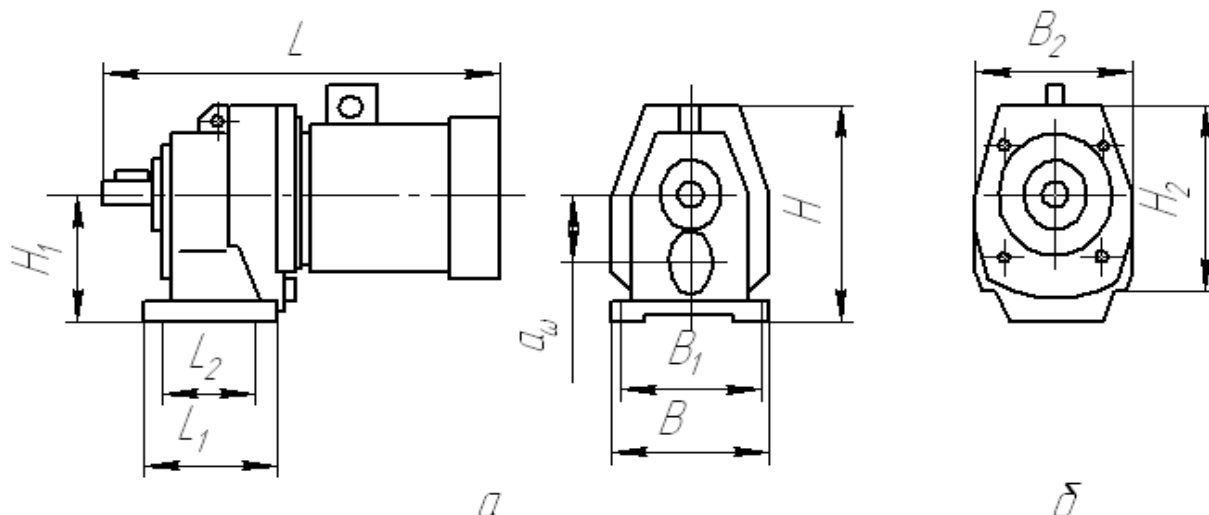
Габаритні і приєднувальні розміри асинхронного циліндричного двохосьового мотор-редуктора:
